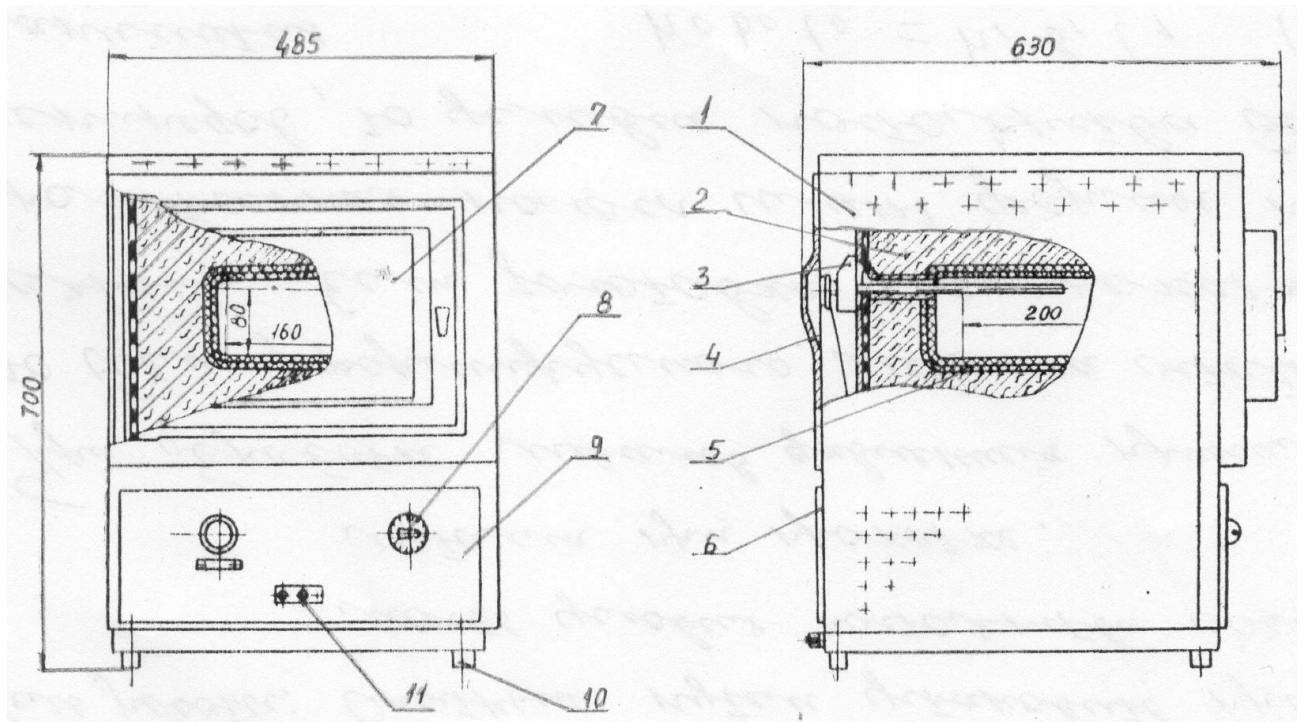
Електропіч СНОЛ-1,6.2,0.0,8/9-М1 (габаритне креслення): 1 - корпус; 2 - теплоізоляція; 3 - терморегулятор; 4 - задній лист; 5 - вузол нагрівача; 6 - лист; 7 - дверцята; 8 - ручка терморегулятора; 9 - блок електричний; 10 - опора; 11 - перемикач.
